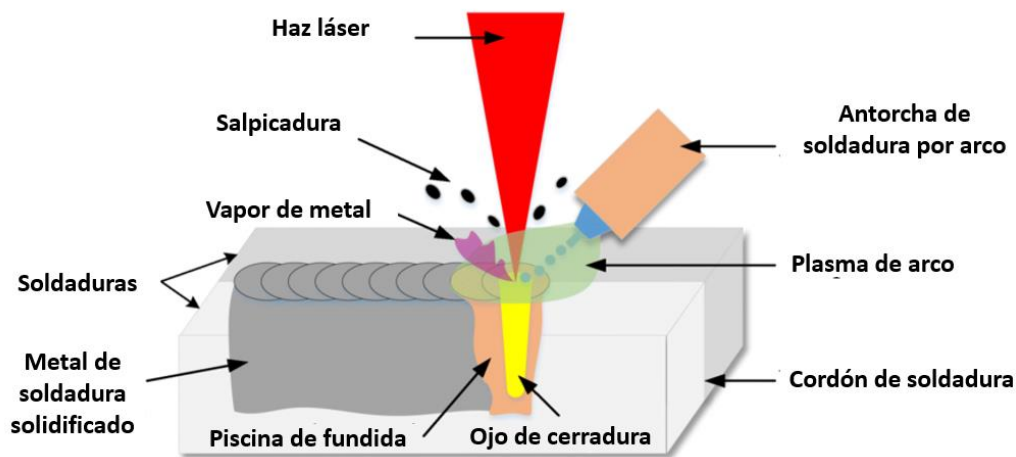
Soldadura híbrida PAW-láser. (Modificado de Fan y col. (2021)).
